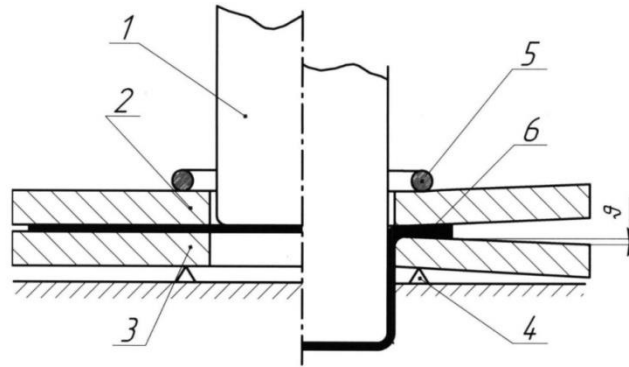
Схема вытяжки с упругими элементами: 1 - пуансон, 2 - прижим, 3 - матрица, 4 - опорное кольцо, 5 - прижимное кольцо, 6 - заготовка
